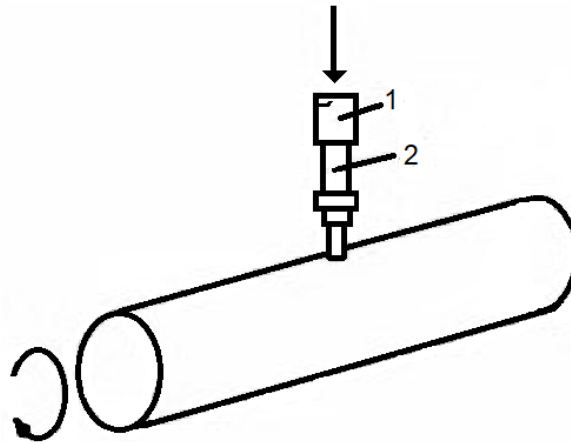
Esquema de máquina espiga sobre cilindro [22].
